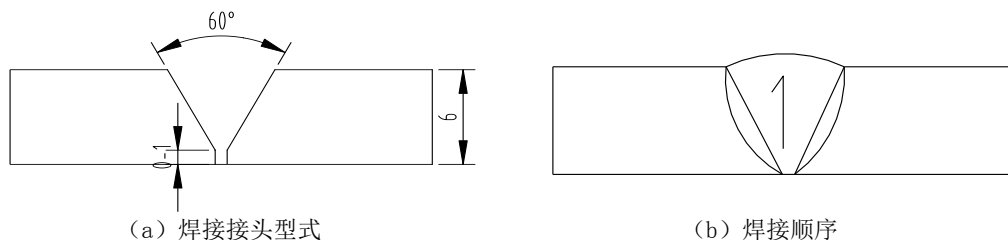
SUS304 自动焊焊接接头型式和焊接顺序
